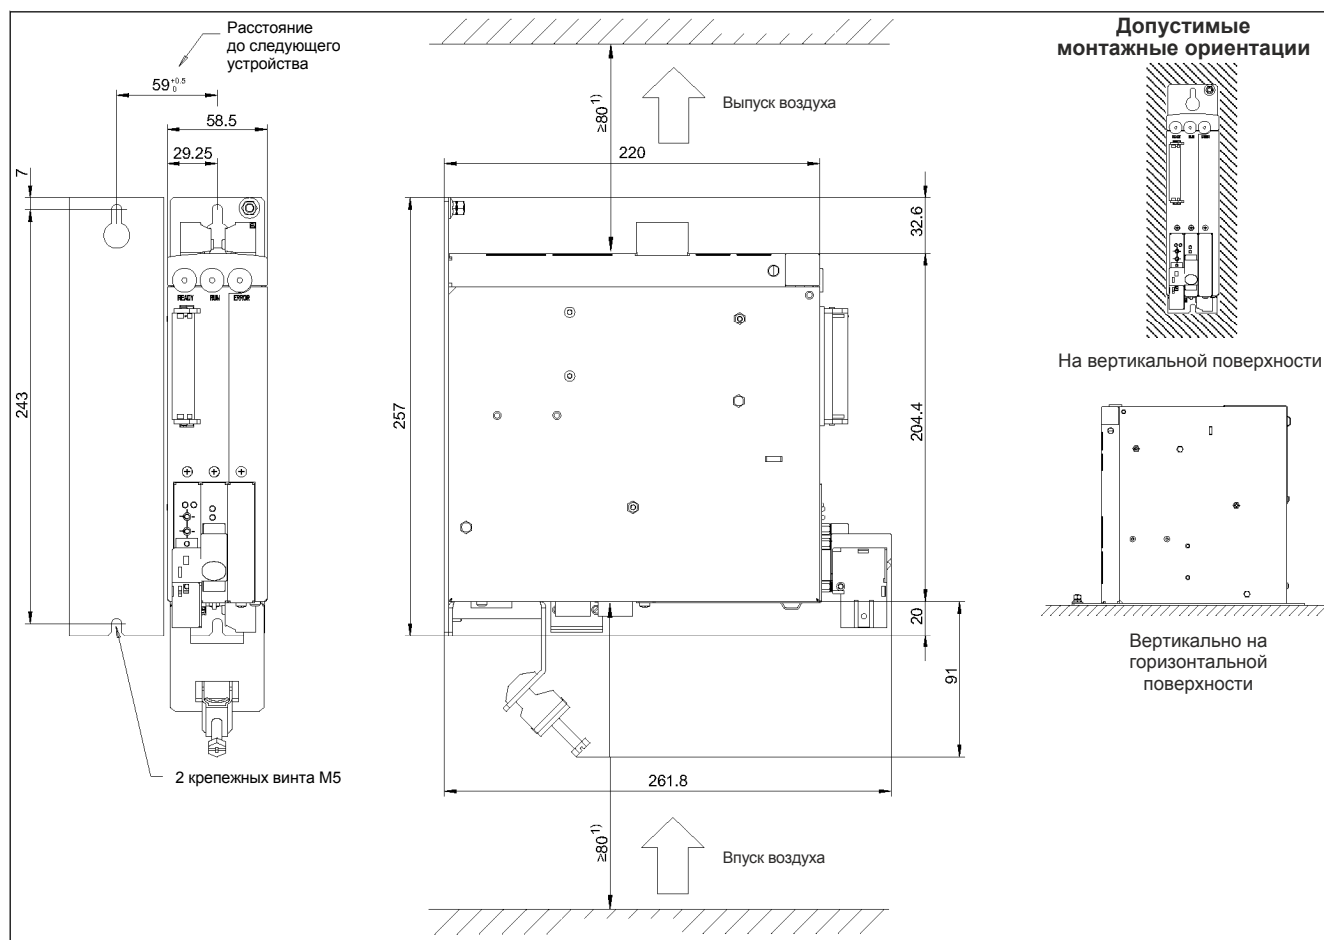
АСОPOS 1010, 1016 – Габаритный чертеж и монтажные размеры
